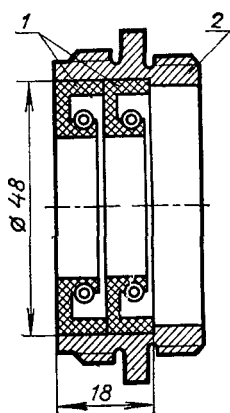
Модернизация гайки крепления подшипников ведущей шестерни:
